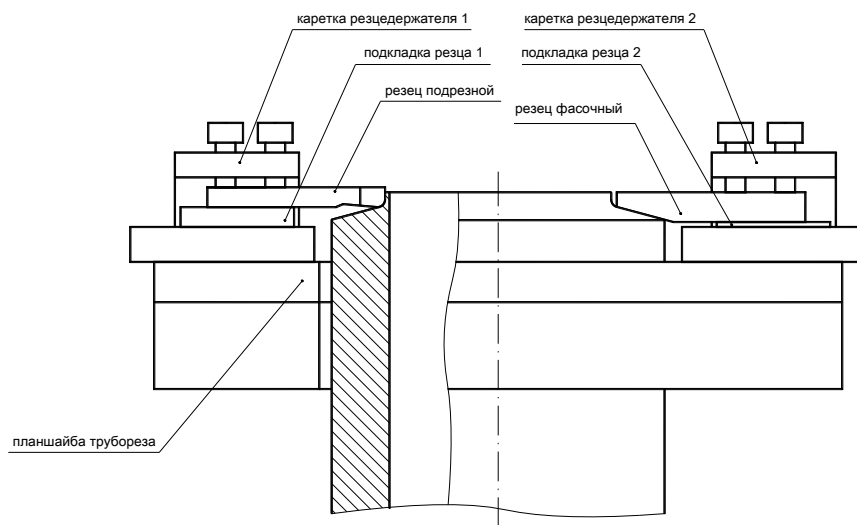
Изготовление комбинированной наружной фаски двумя резцами
